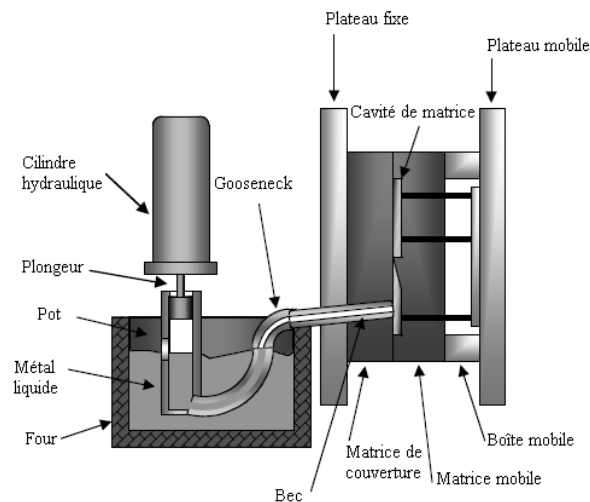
Machine de moulage mécanique sous pression avec chambre chaude [1].
